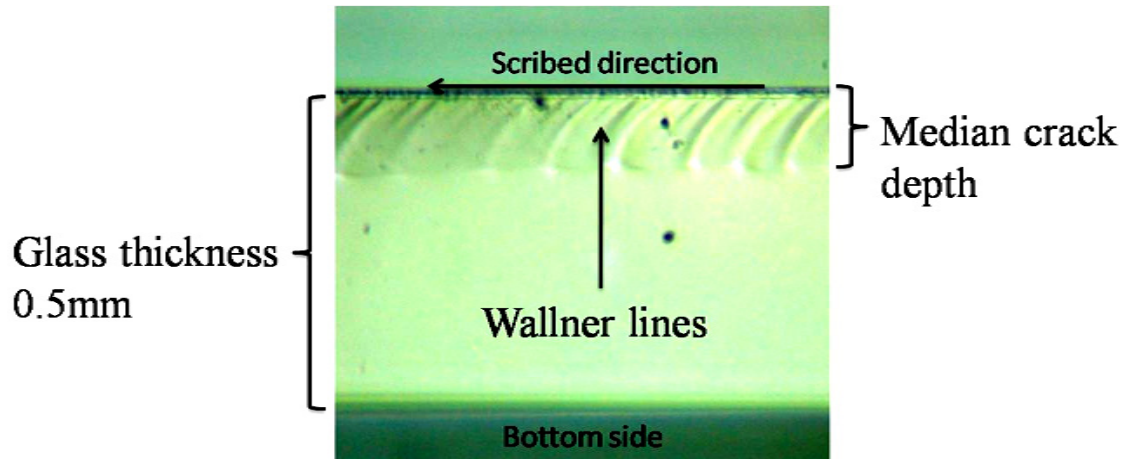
Wallner line。玻璃切割後之側視圖，顯示代表中央裂紋深度的 Wallner line。
